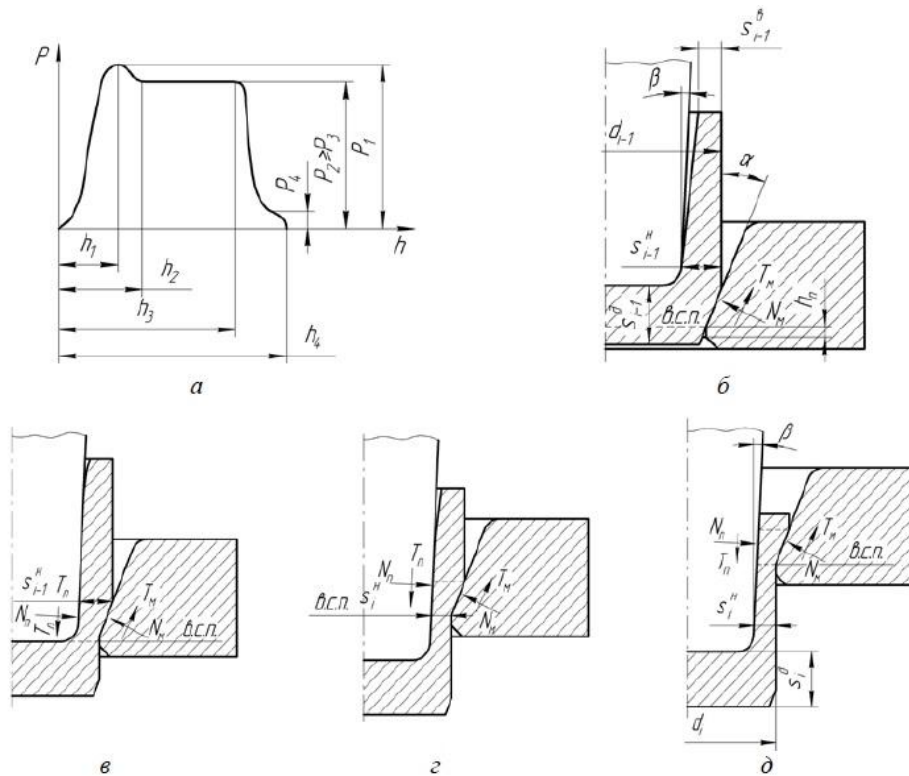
Машинна діаграма «зусилля – шлях інструмента» $P-h(a)$ і схема формозміни заготовки по стадіям процесу витягування з потоншенням через одну матрицю(б-д)
